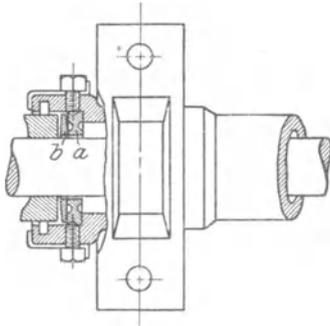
Fettbüchse mit Anlaufring und Verschleißring.
